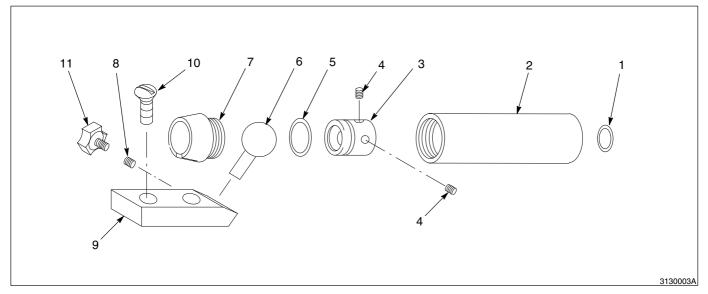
Kugelmontagekit für Fertigungslinie
